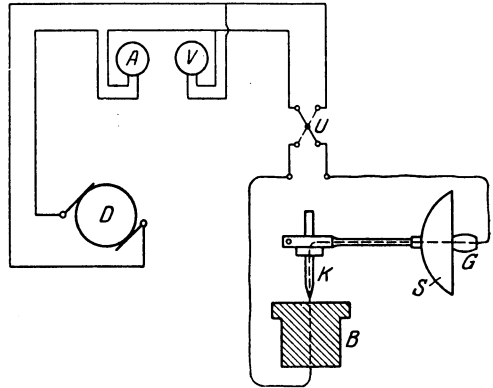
Schema einer Lichtbogenschweißanlage.
